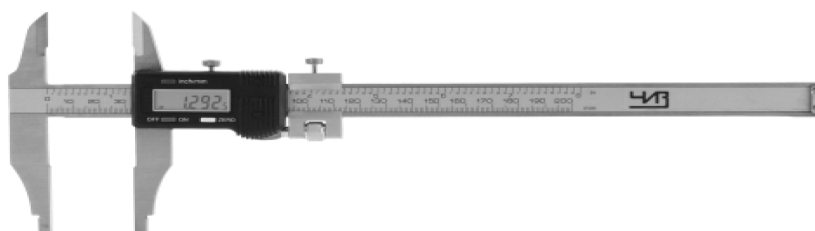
Общий вид штангенциркулей ШЦЦ-II
